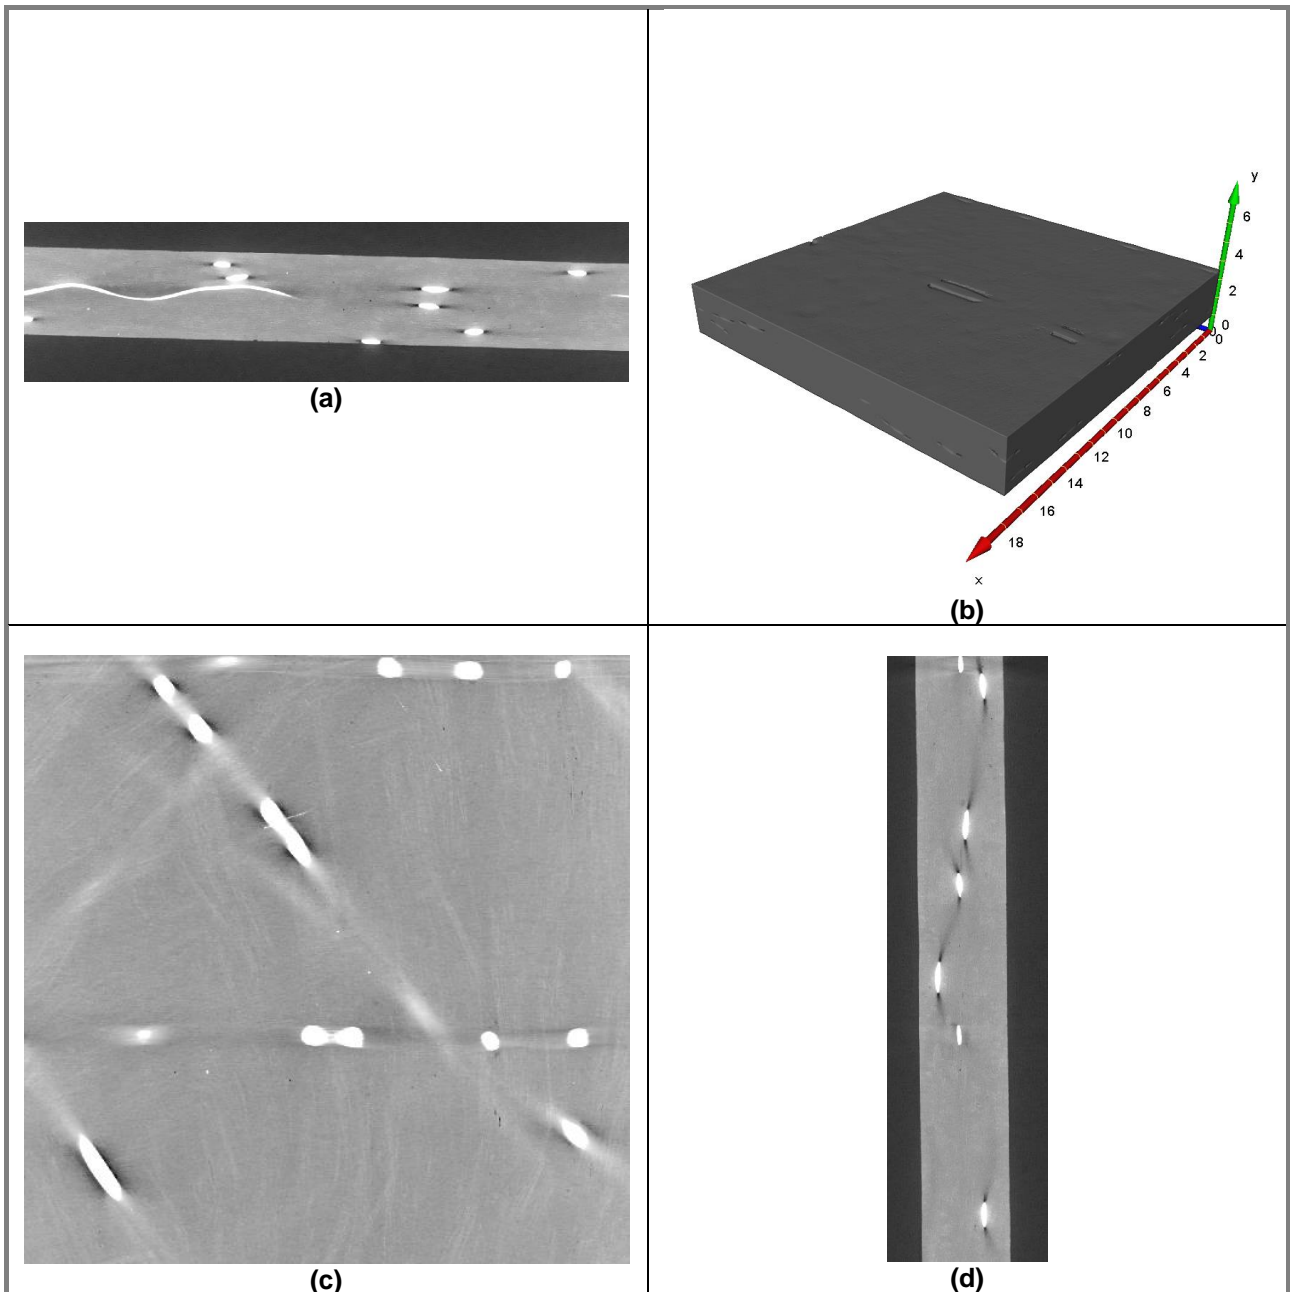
Campione N°1; sezione xy (a); sezione xz (c); sezione yz (d); ricostruzione 3D (b).
